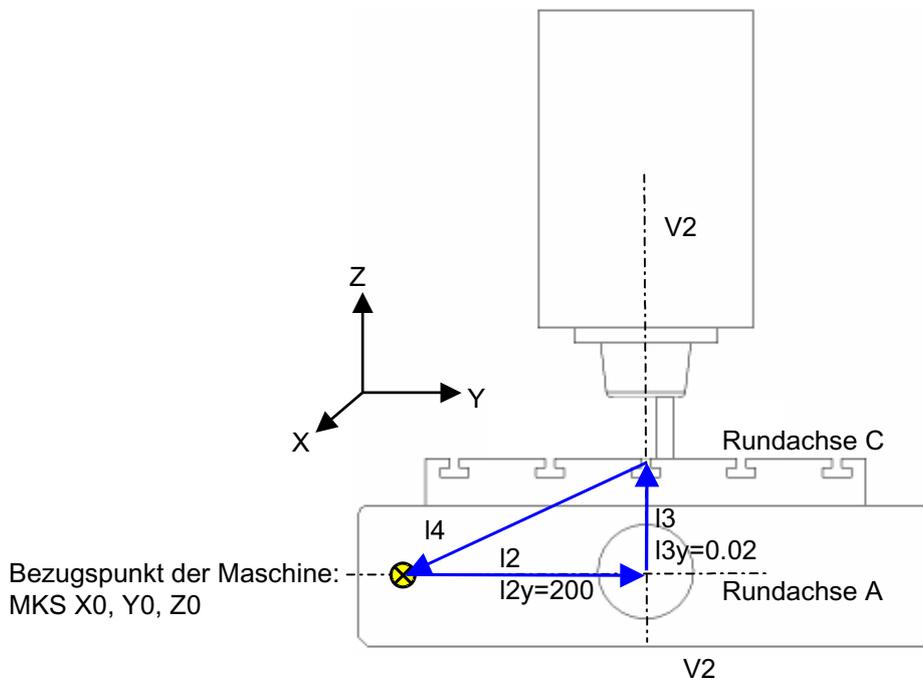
Schwenktisch "TABLE\_5" (Seitenansicht)
